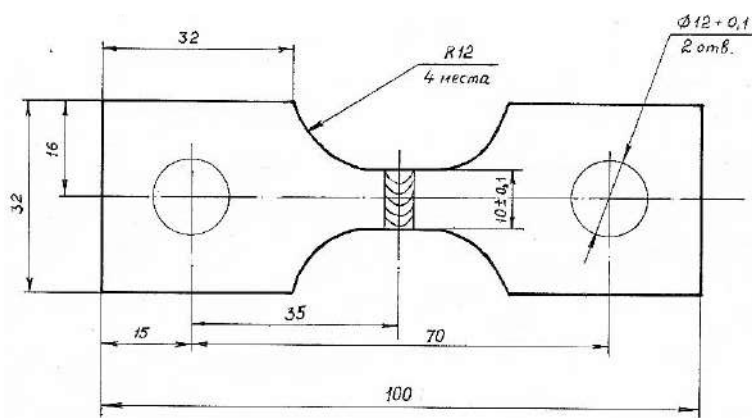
Эскиз образца для циклических испытаний сварных соединений
